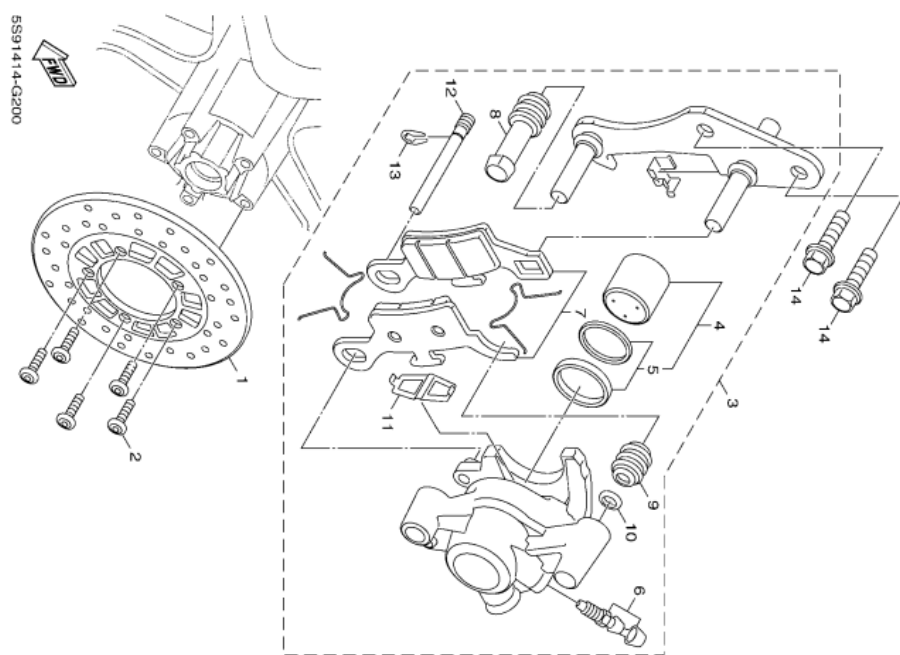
CALIBRE FRENO DELANTERA FRONT BRAKE CALIPER
